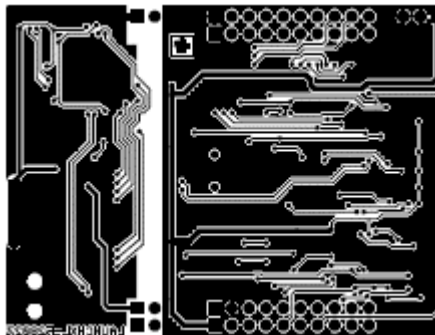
Disposition du PCB LAUNCHXL-F28027 - Couche inférieure
